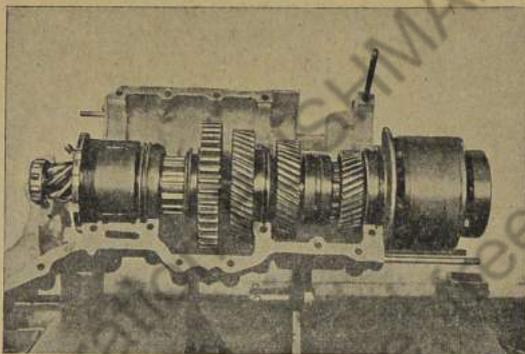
Hauptwelle-Zusammenbau in rechte Gehäusehälfte einlegen
